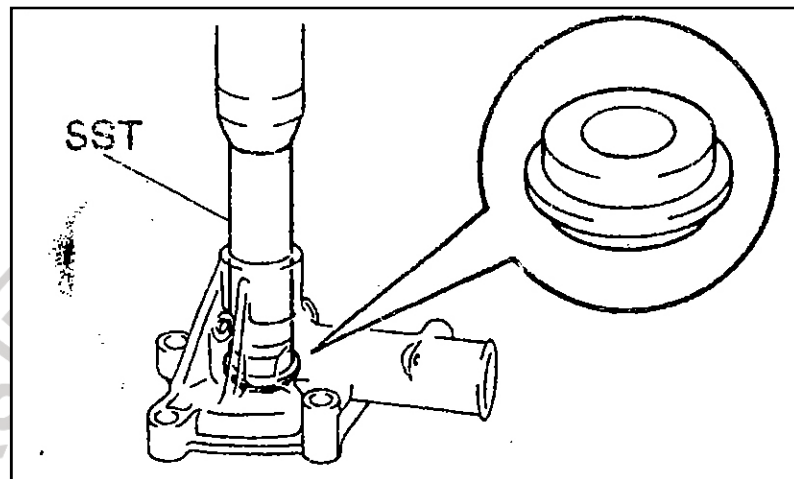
Melepas Bearing Pompa Air dan Rotor
